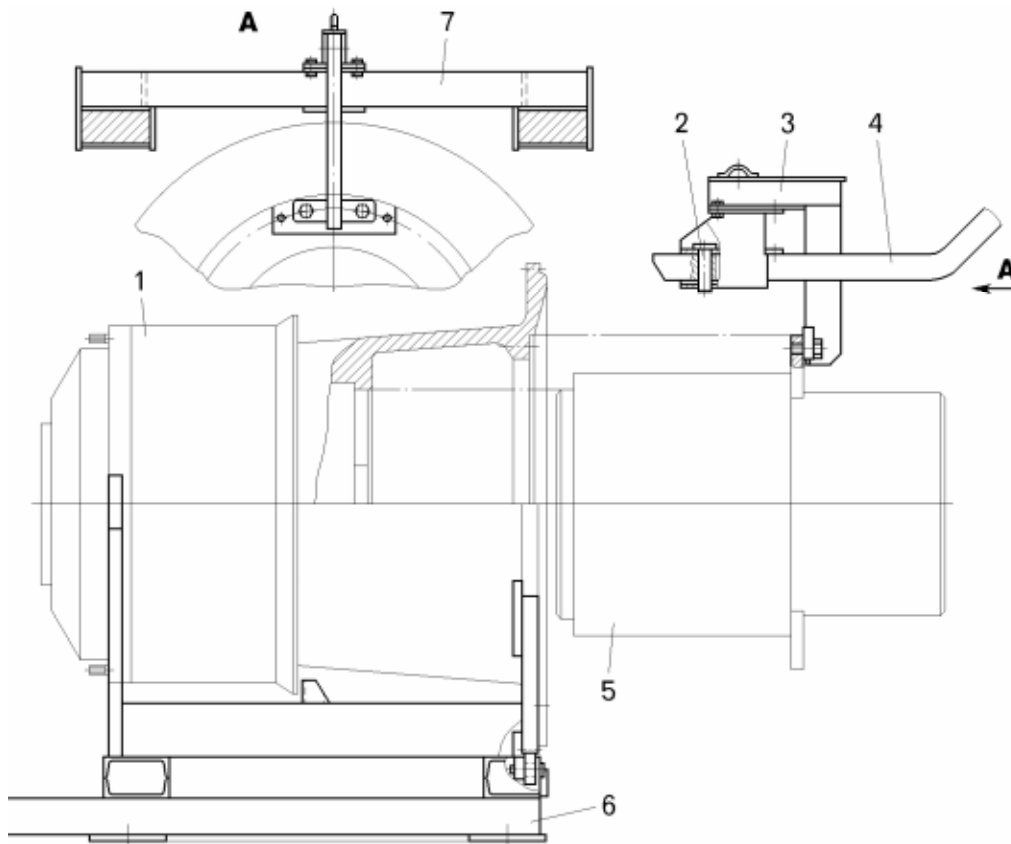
Приспособление для установки и снятия тягового электродвигателя:
